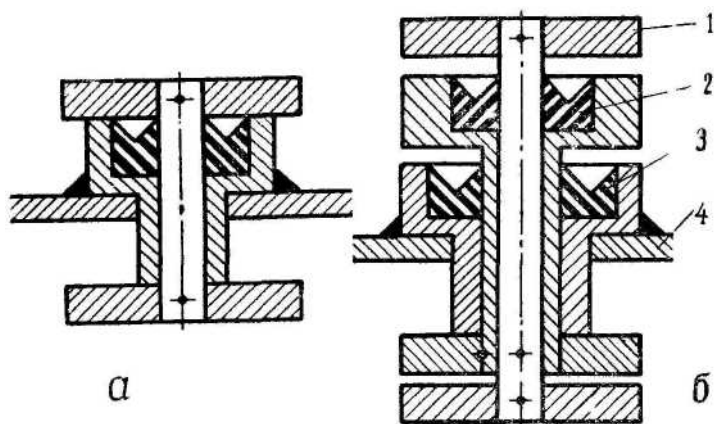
Герметизация валиков: а — с простой рукояткой; б — с двойной рукояткой: 1 — рукоятка; 2 — резиновое кольцо (5×12×5); 3 — кольцо (8×16×6); 4 — корпус
